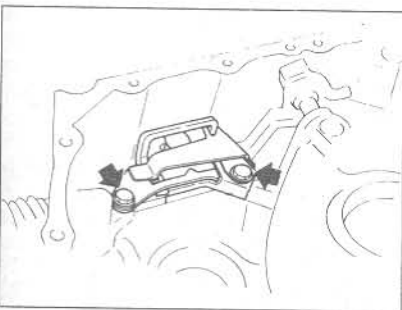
Снятие сборки фиксатора заднего хода (Глава 12)
